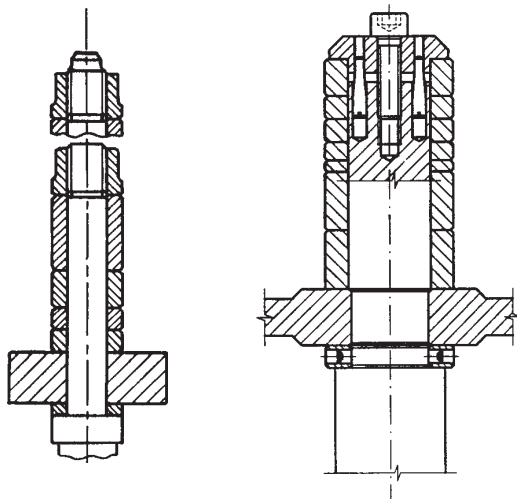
Spindel – Beispiele für Werkzeugbefestigung
